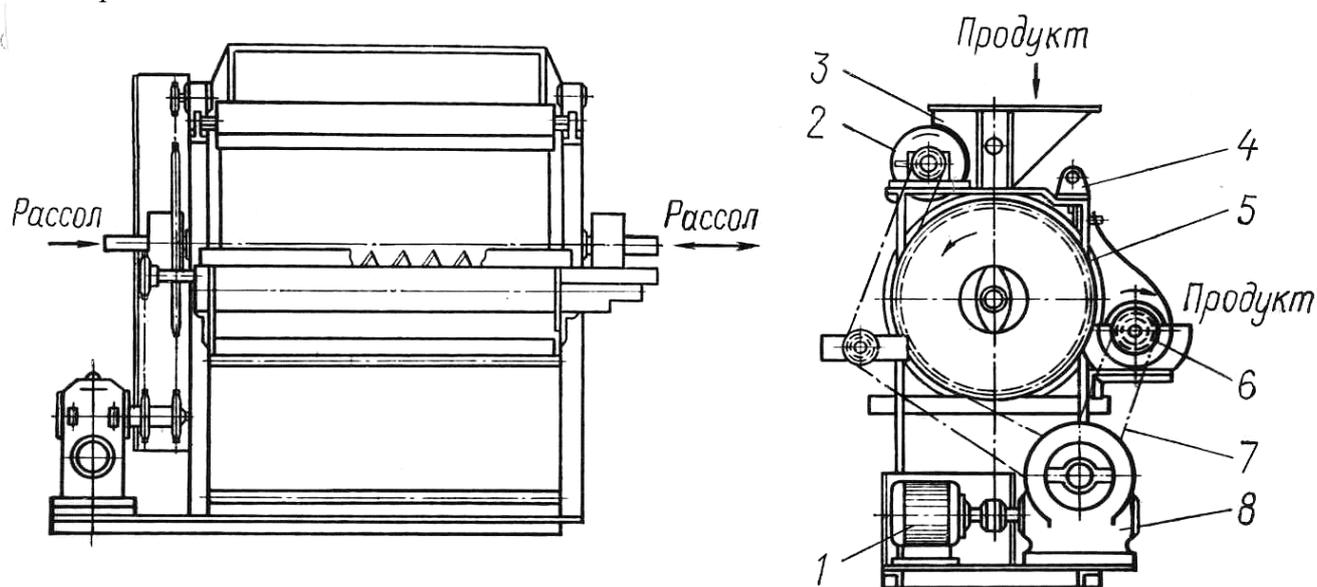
Открытый охладитель творага: 1 – электродвигатель; 2 – валик; 3 – бункер; 4 – нож; 5 – барабан; 6 – шнек; 7 – цепная передача; 8 – червячный редуктор
